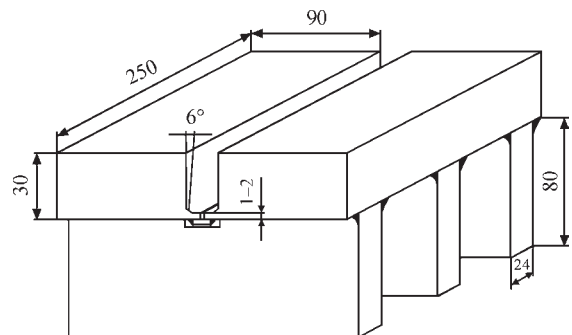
Жорстка проба для виконання зварного стикового з'єднання сталі СА-6NM
